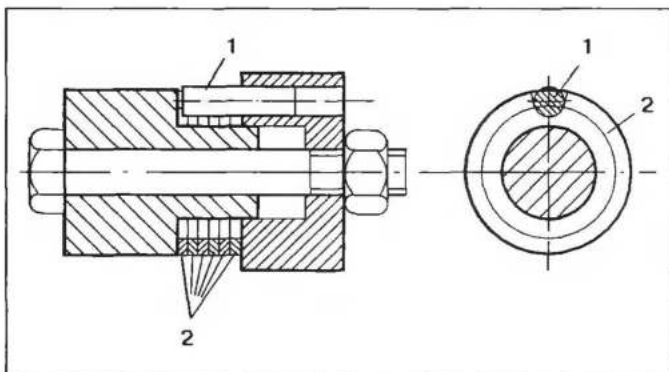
Оправка для термофиксации уплотнительных колец: 1 — шпонка; 2 — кольцо
